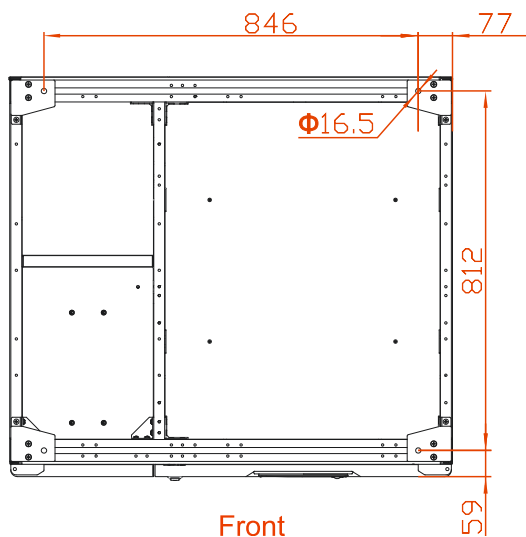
Вид снизу на установочный пьедестал KR33300, KR33400
